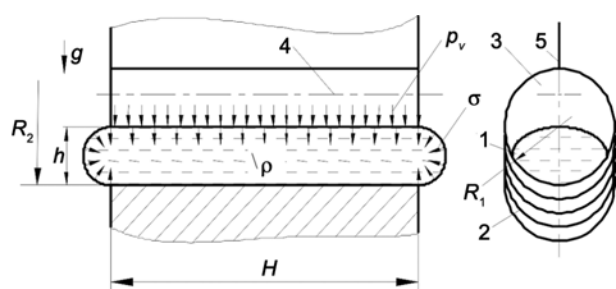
Модель канала проплавления при ЭЛС горизонтальным пучком на подъем: 1 – сварочная ванна; 2 – сварной шов; 3 – пароголовый канал; 4 – ось пучка; 5 – стык
